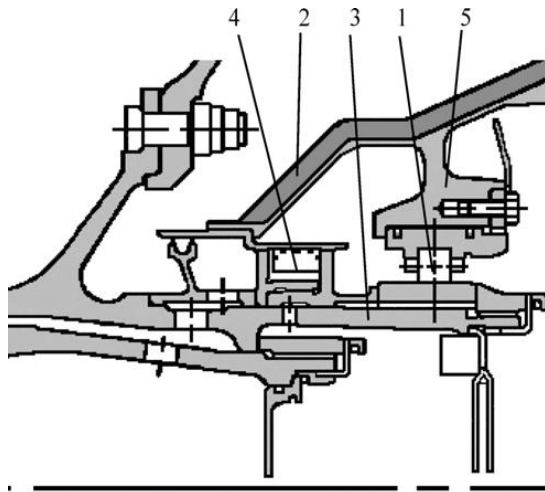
Задня опора ротора НД с роликоподшипником
